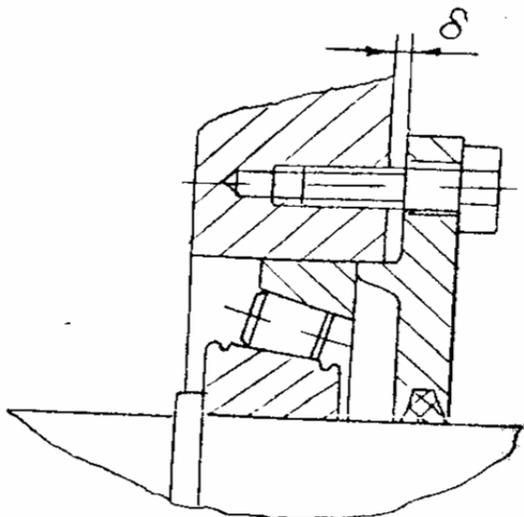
Определения толщины пакета прокладок для регулировки осевой игры подшипника
